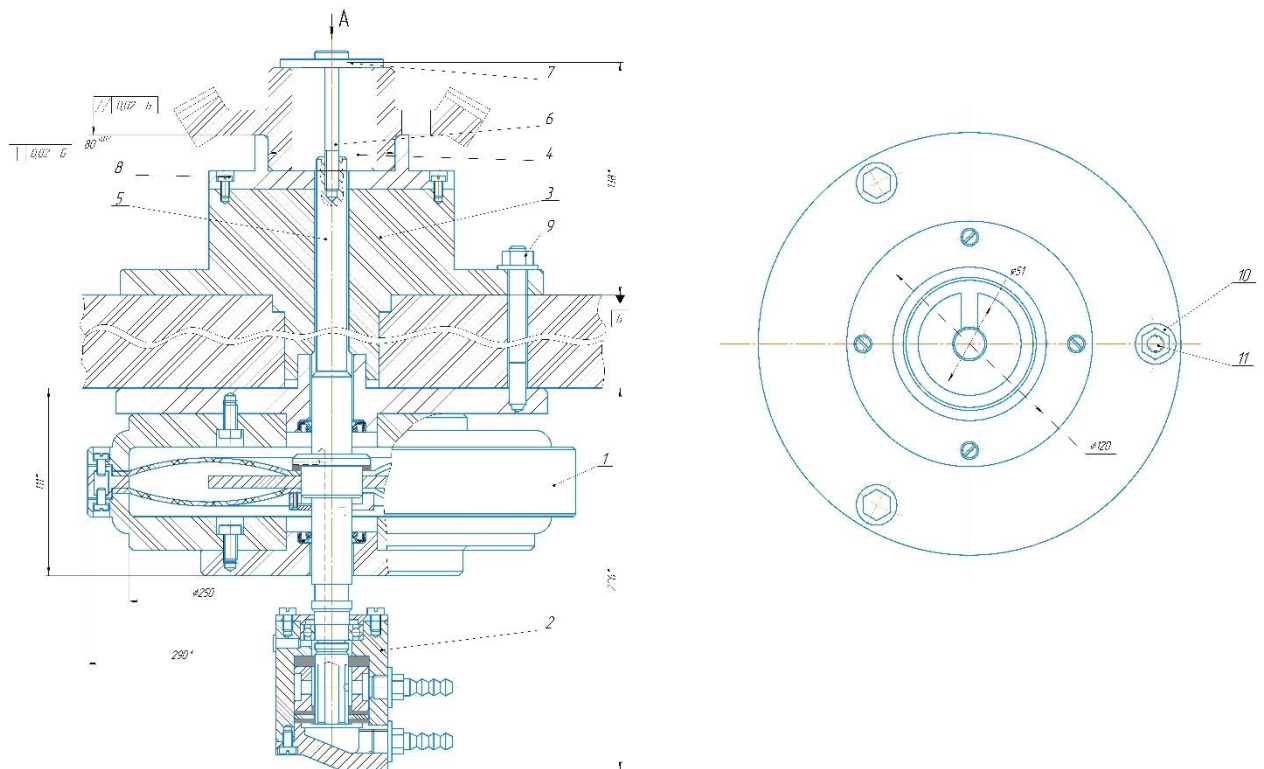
Конструкція спеціального пристосування для фрезерування зубців
